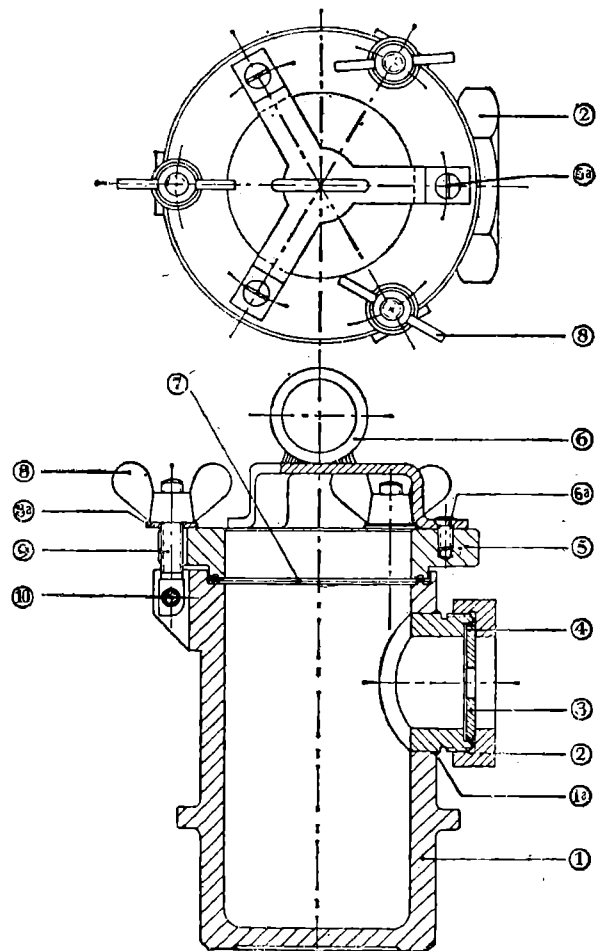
Recipiente a presión montado; vistas esquemáticas en sección vertical y en planta.
